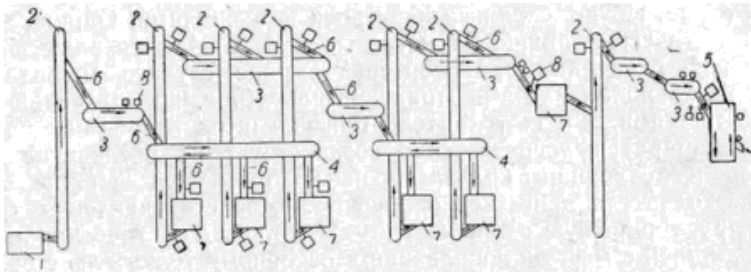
Компонування токарної ділянки автоматичного цеху по виготовленню підшипників.
